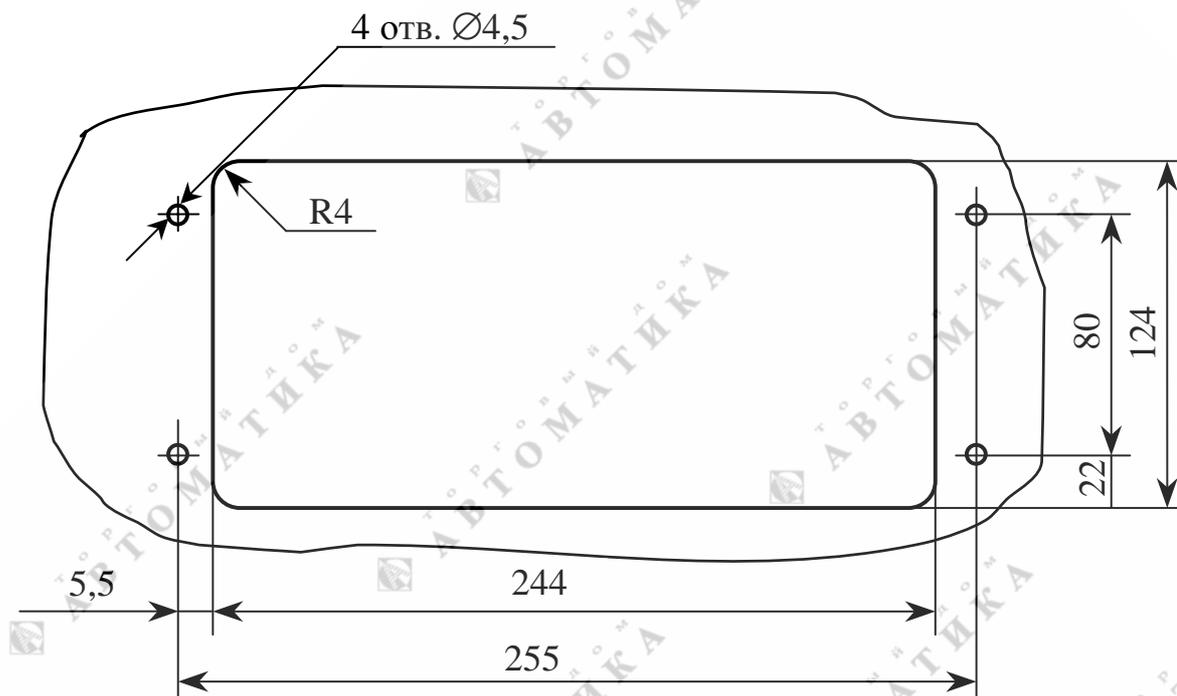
Разметка отверстий в щите для крепления блока преобразовательного
